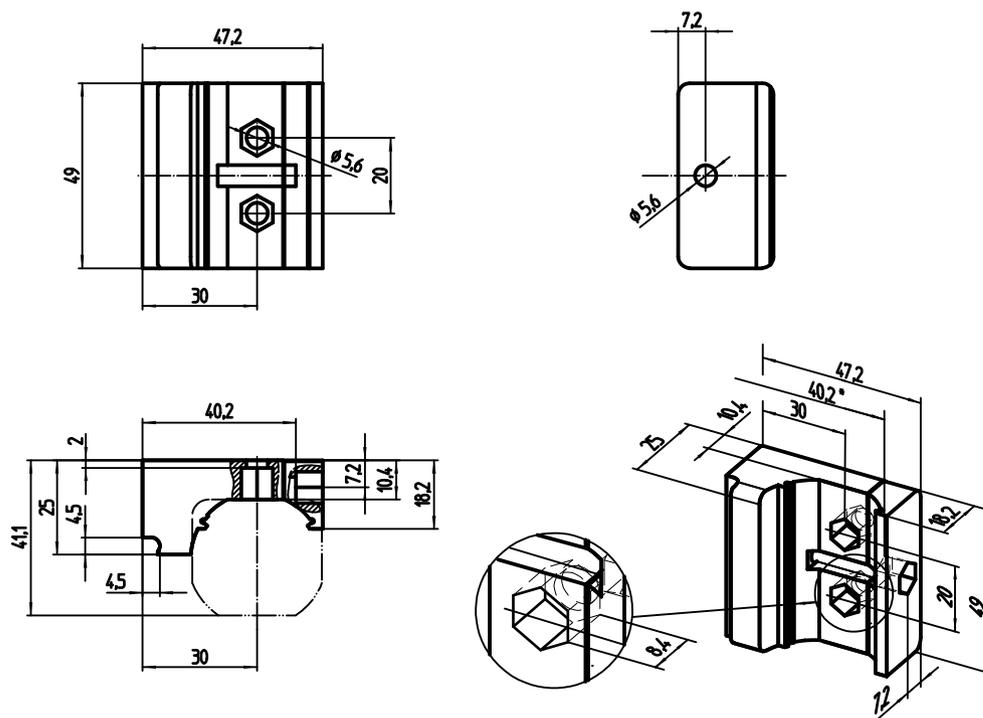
Габаритный чертеж крепления QuickFix (2066048)
